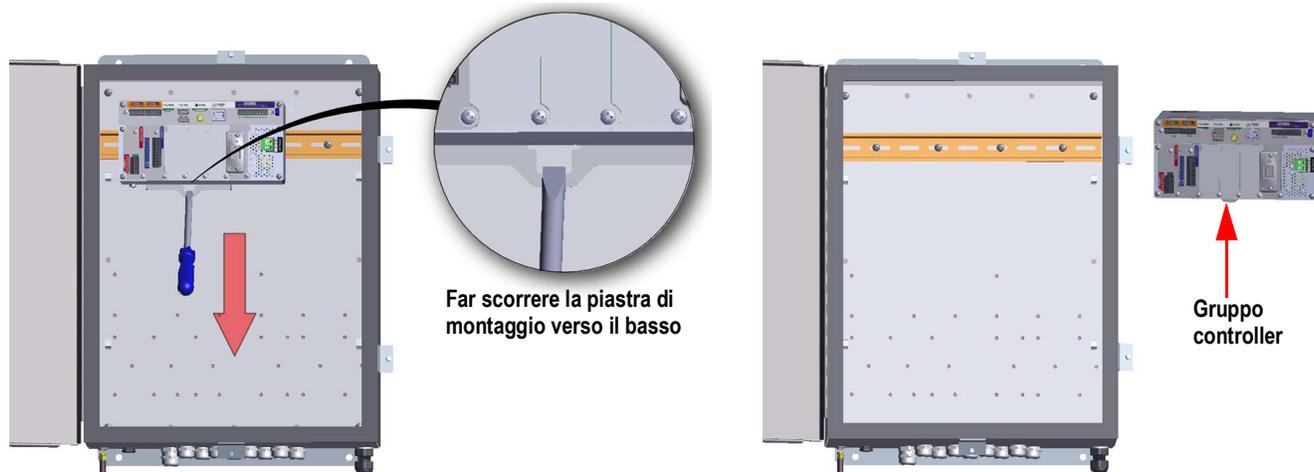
Rimuovere il gruppo controller - Montaggio a parete
